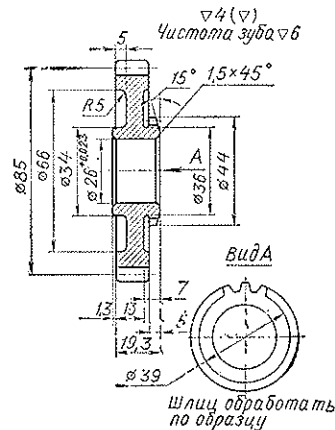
Вторичный вал к спортивной коробке передач. Шестерня второй передачи. Данные для изготовления; число зубьев — 34; m — 2,5; α — 20°; D_{e2} — 81,1; h — 5,625; d — d_2 — 75
